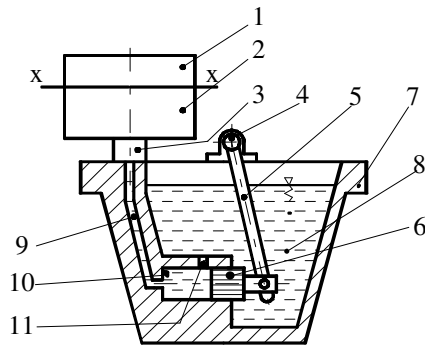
Mașina de turnat cu cameră caldă cu piston orizontal:
